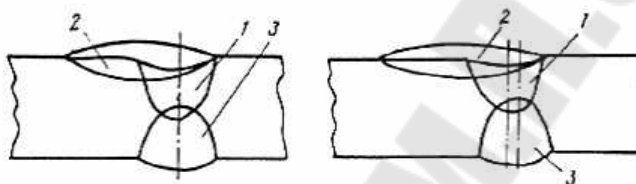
Внешний вид макрошлифов сварных швов при двухсторонней автоматической сварке под флюсом и симметричном и несимметричном расположении первого (наружного) и внутреннего слоев шва: 1 - первый (наружный) слой шва; 2 - облицовочный слой шва; 3 - внутренний слой шва
